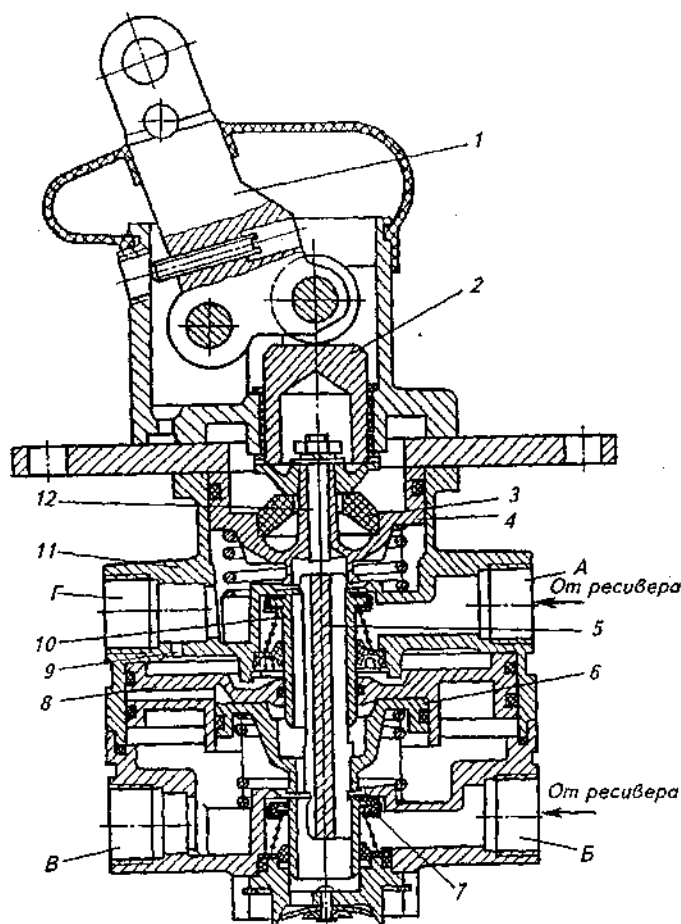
Двухсекционный тормозной кран: А, Б, В, Г—выводы; 1 — рычаг; 2 — толкатель; 3 — резиновая втулка; 4 — верхний следящий поршень; 5—полый шток; 6—нижний следящий поршень; 7, 10— клапаны; 8—большой поршень; 9—отверстие; 11 — корпус; 12 — упорный болт
